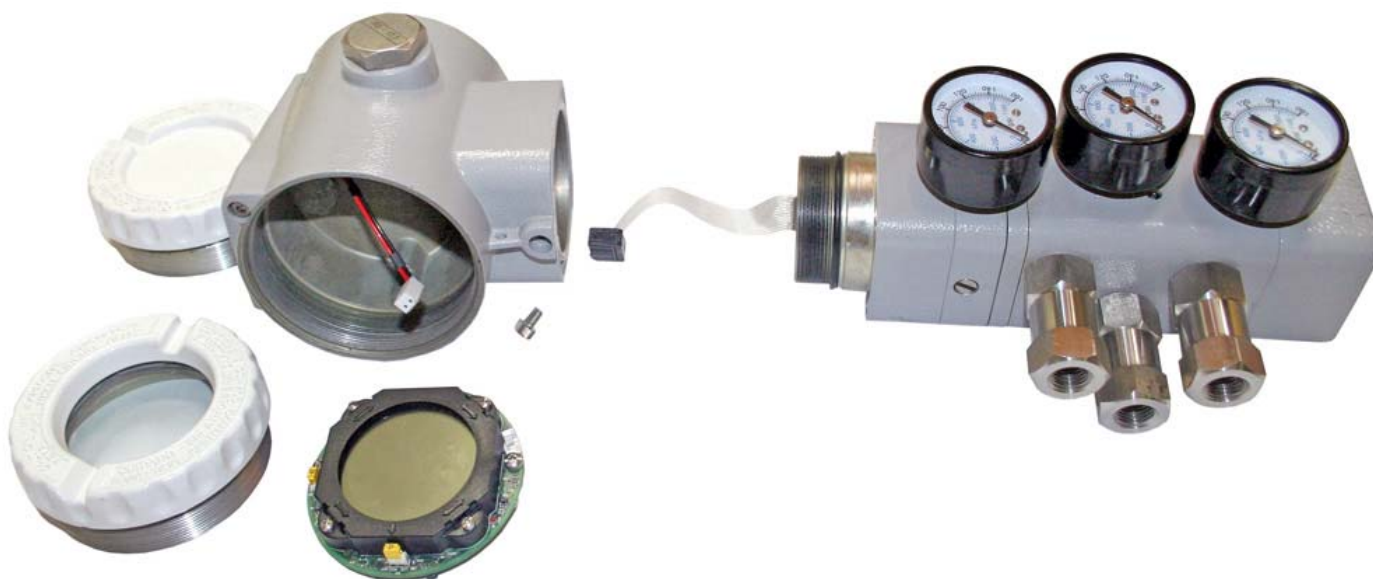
Carcaça desmontada, separada do Transdutor
